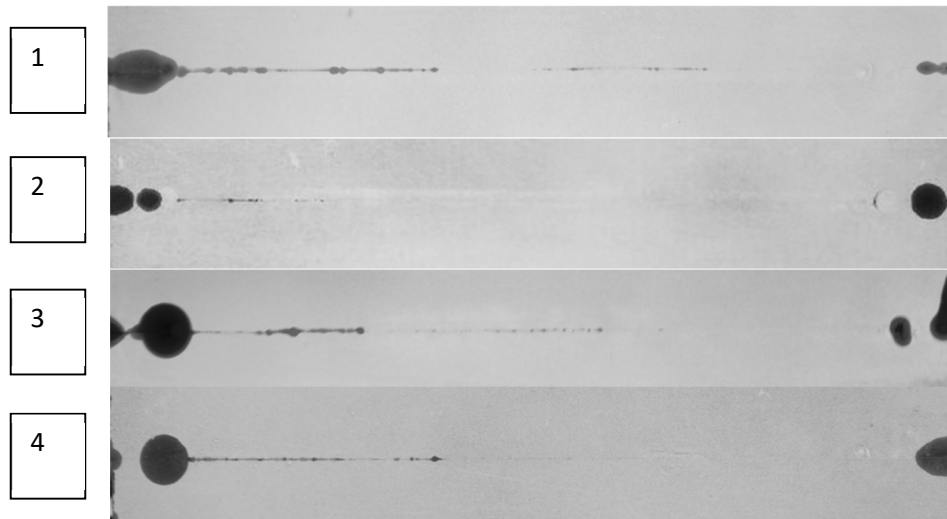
Indicaciones de LP sobre cordones de soldadura obtenidos mediante FSW De arriba abajo 90 mm/min – 1085 RPM, 127 mm/min – 1400 RPM, 45 mm/min – 1085 RPM y 187 mm/min – 1400 RPM.
